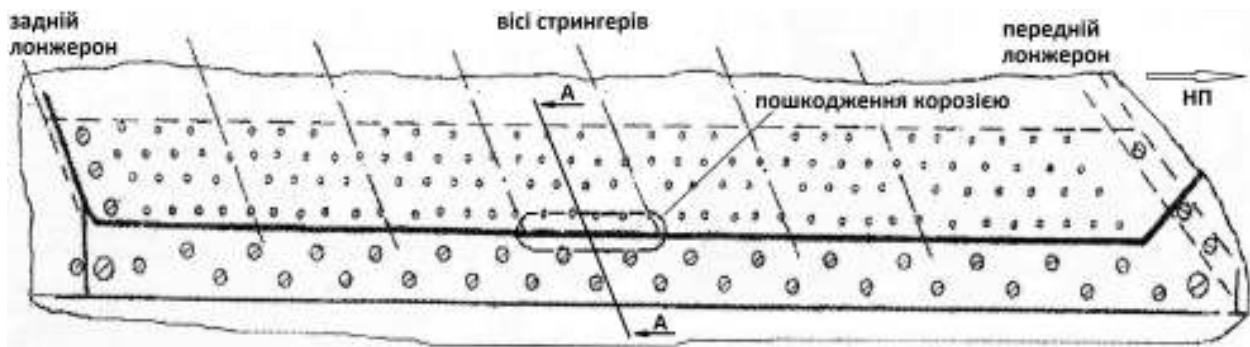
Схема конструкцій кріплення кіля до підкільової надбудови
